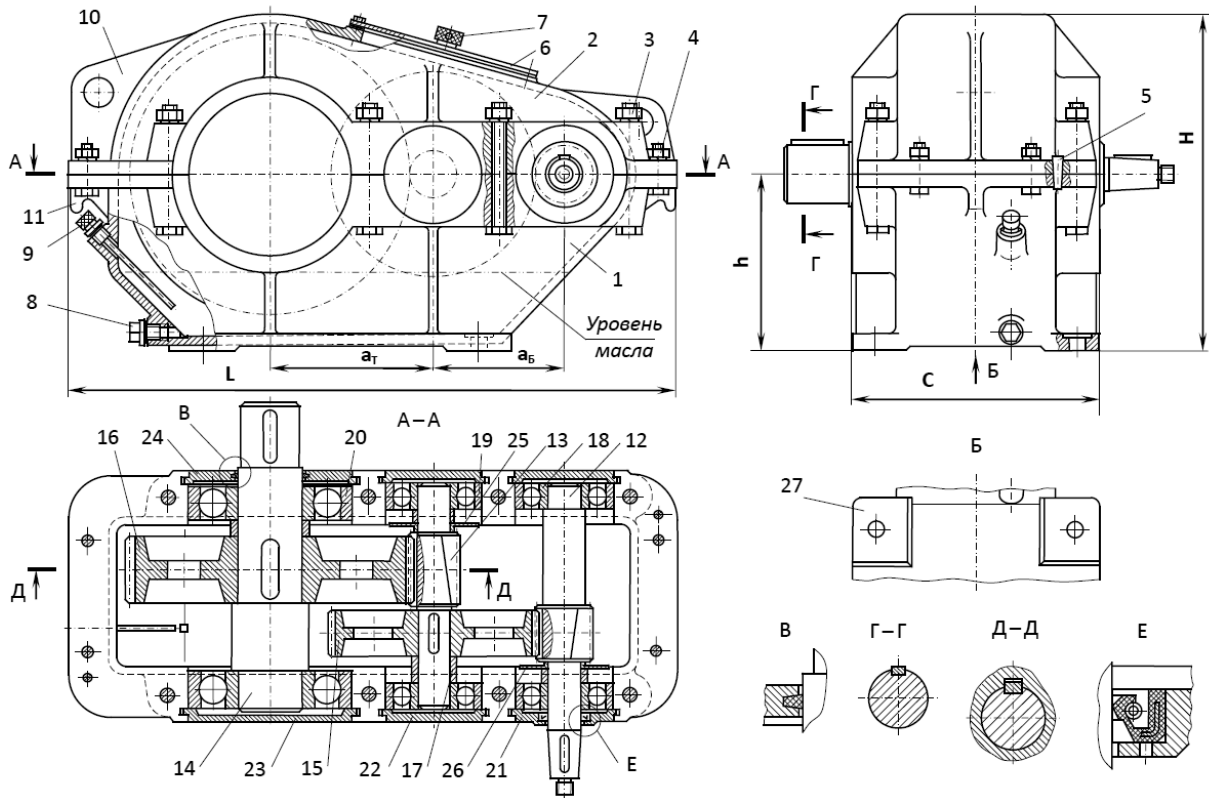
Двухступенчатый горизонтальный цилиндрический редуктор
